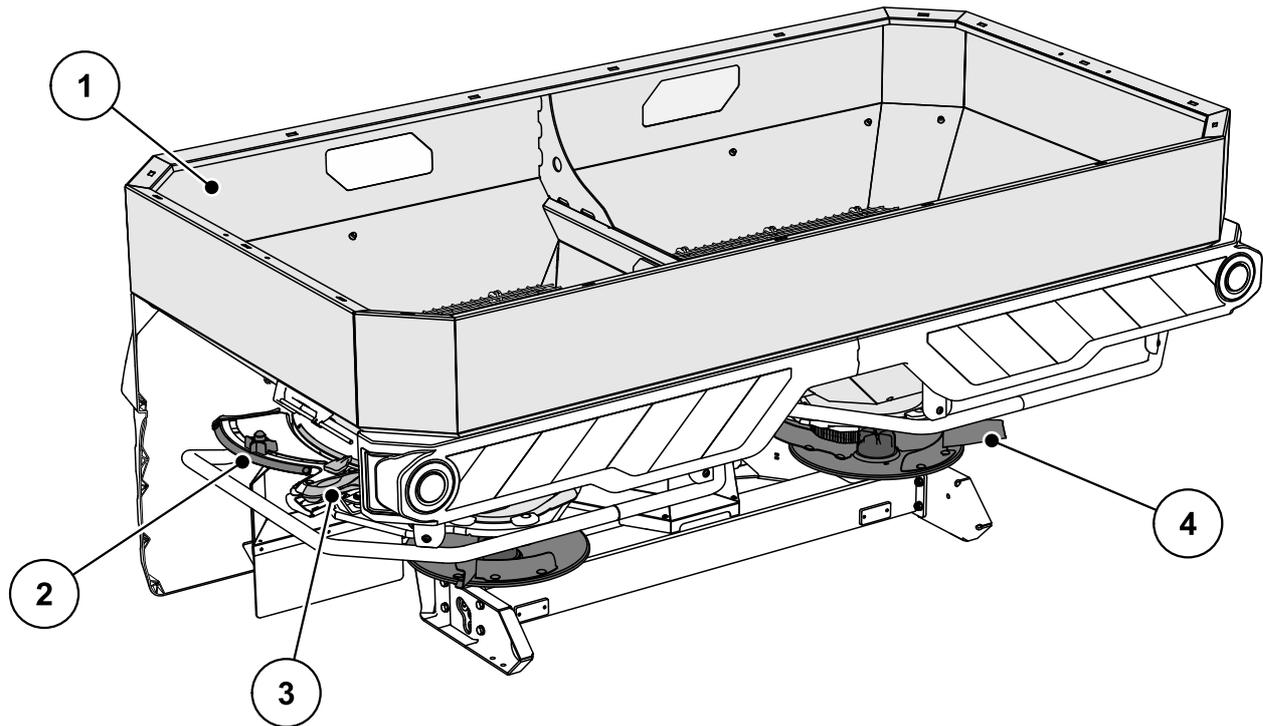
Aperçu des composants : Exemple AXIS 30.2 - vue arrière
